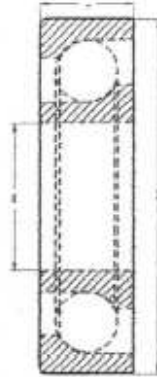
, Rodamiento de Bolas de contacto Angular, fuente, López William.
